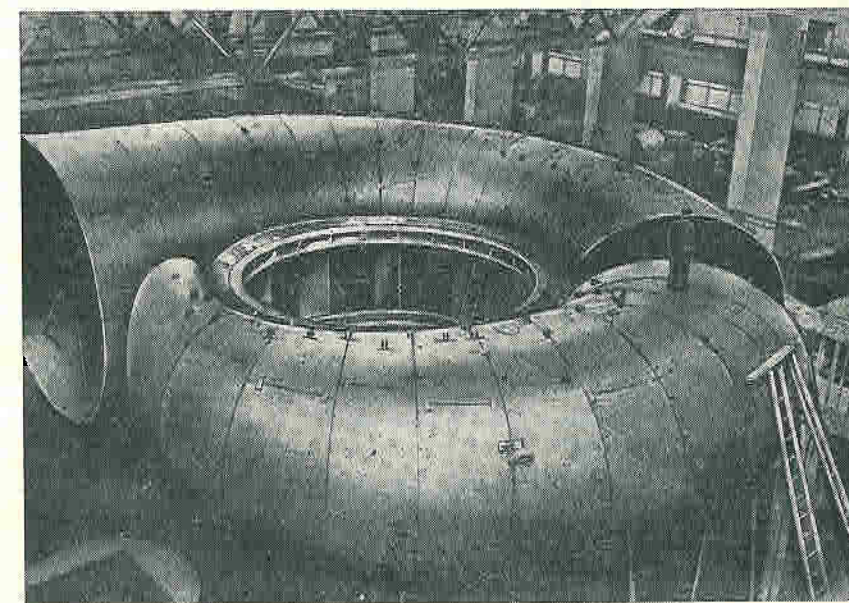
Контрольная сборка спиральной камеры на заводе-изготовителе
